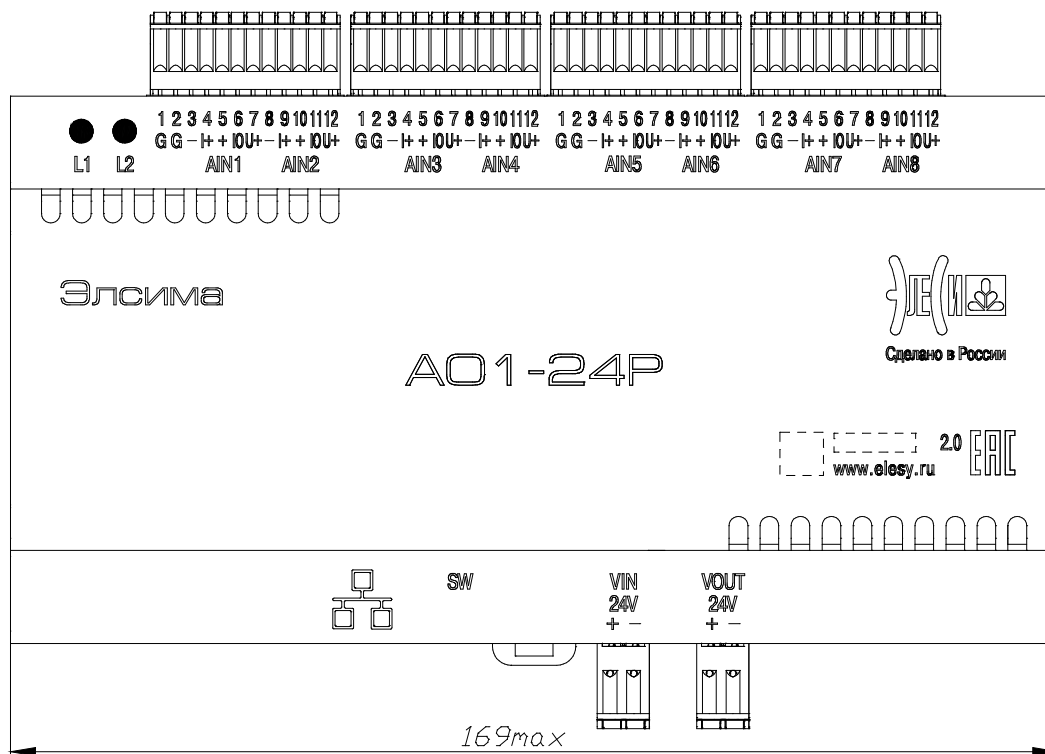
Модуль УВВ. Габаритный чертеж. Вид спереди
